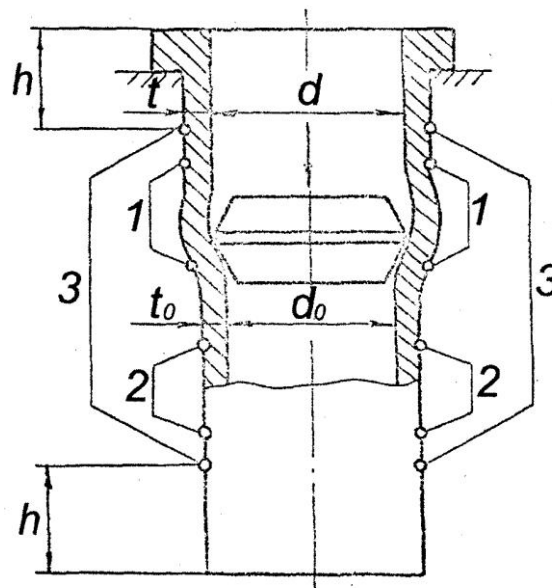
Визначення осьових деформацій обробленої заготовки
